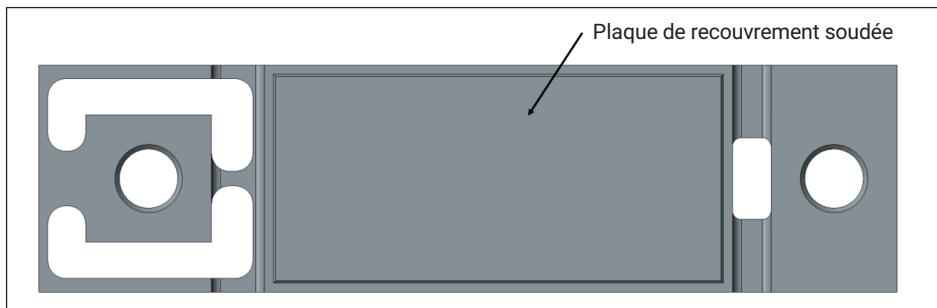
Plaque de recouvrement soudée hermétiquement en face supérieure du capteur
